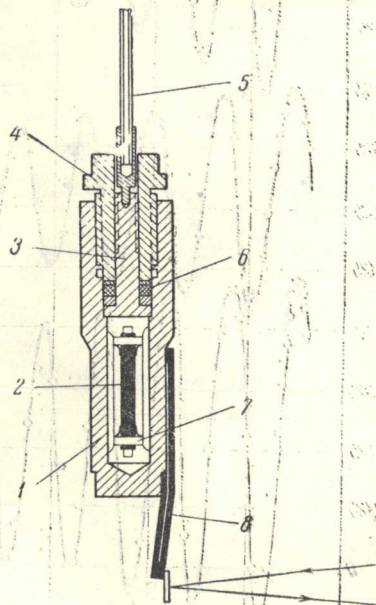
Устройство бомбы: 1 — корпус, 2 — образец, 3 — грибок, 4 — пробка, 5 — стеклянный стержень, 6 — уплотняющие прокладки, 7 — держатель образца, 8 — индикатор давления с зеркальцем
